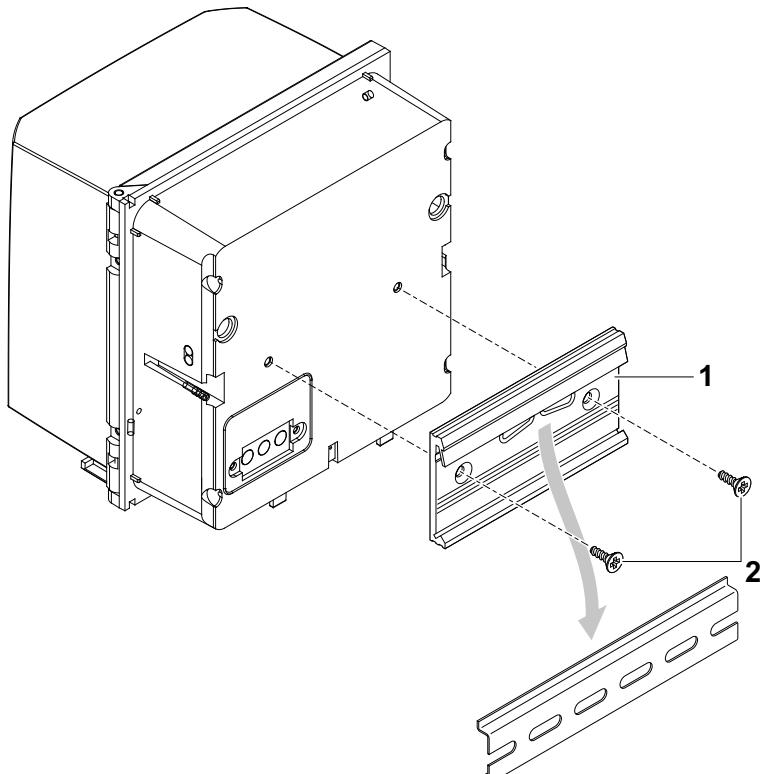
Montagem de DIQ/S 28X em calha DIN
